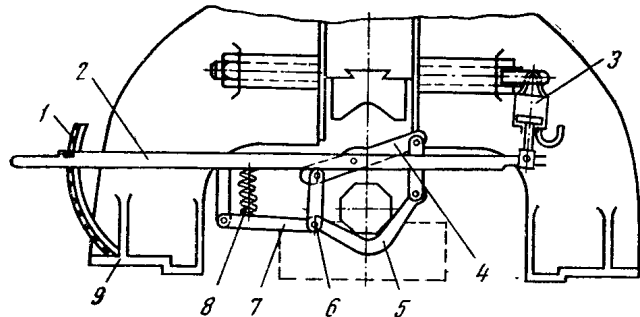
Механический рычажный кантователь к ковочному молоту:
